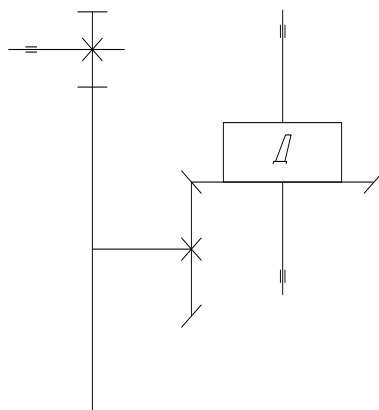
Схема головної передачі : перший ступінь - циліндричний, другий - конічний
